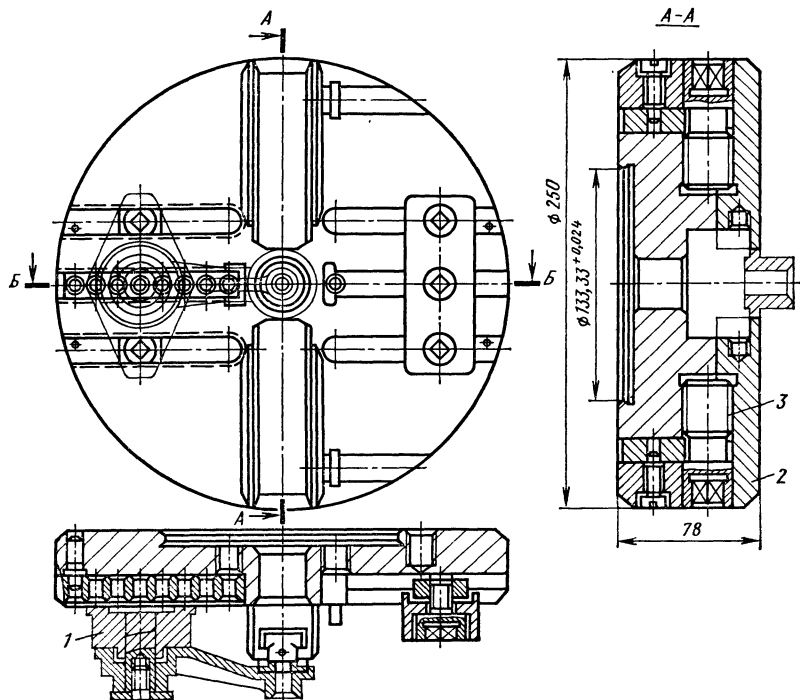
Специализированное наладочное приспособление для обработки второго отверстия деталей типа рычагов
